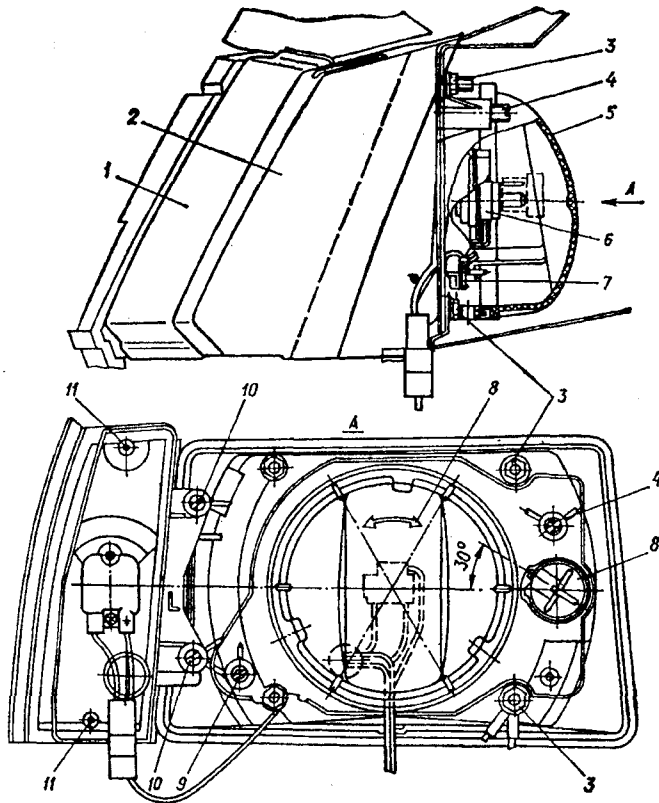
Блок-фара (установка): 1 – блок-фара; 2 – указатель поворота; 3 – гайка крепления фары; 4 – винт вертикальной регулировки; 5 – крышка; 6 – лампа фары; 7 – лампа стояночного света; 8 – заглушка корректировки светового пучка в зависимости от нагрузки автомобиля; 9 – винт горизонтальной регулировки; 10 – винт крепления указателя поворота; 11 – винт крепления рассеивателя указателя поворота
